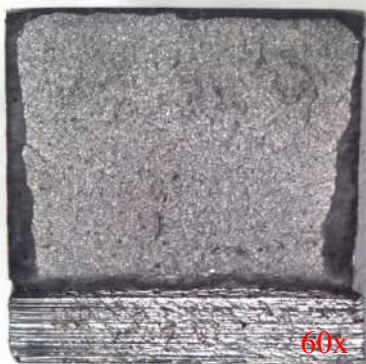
Vista macroscópica de la fractura 22MnB5, -38°C, condición 2.
